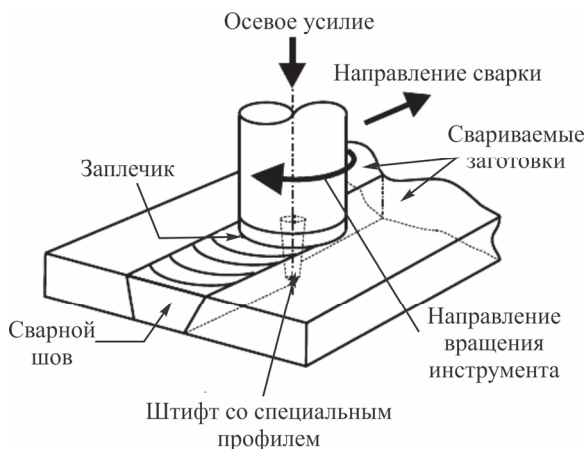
Процесс сварки трением с перемешиванием
